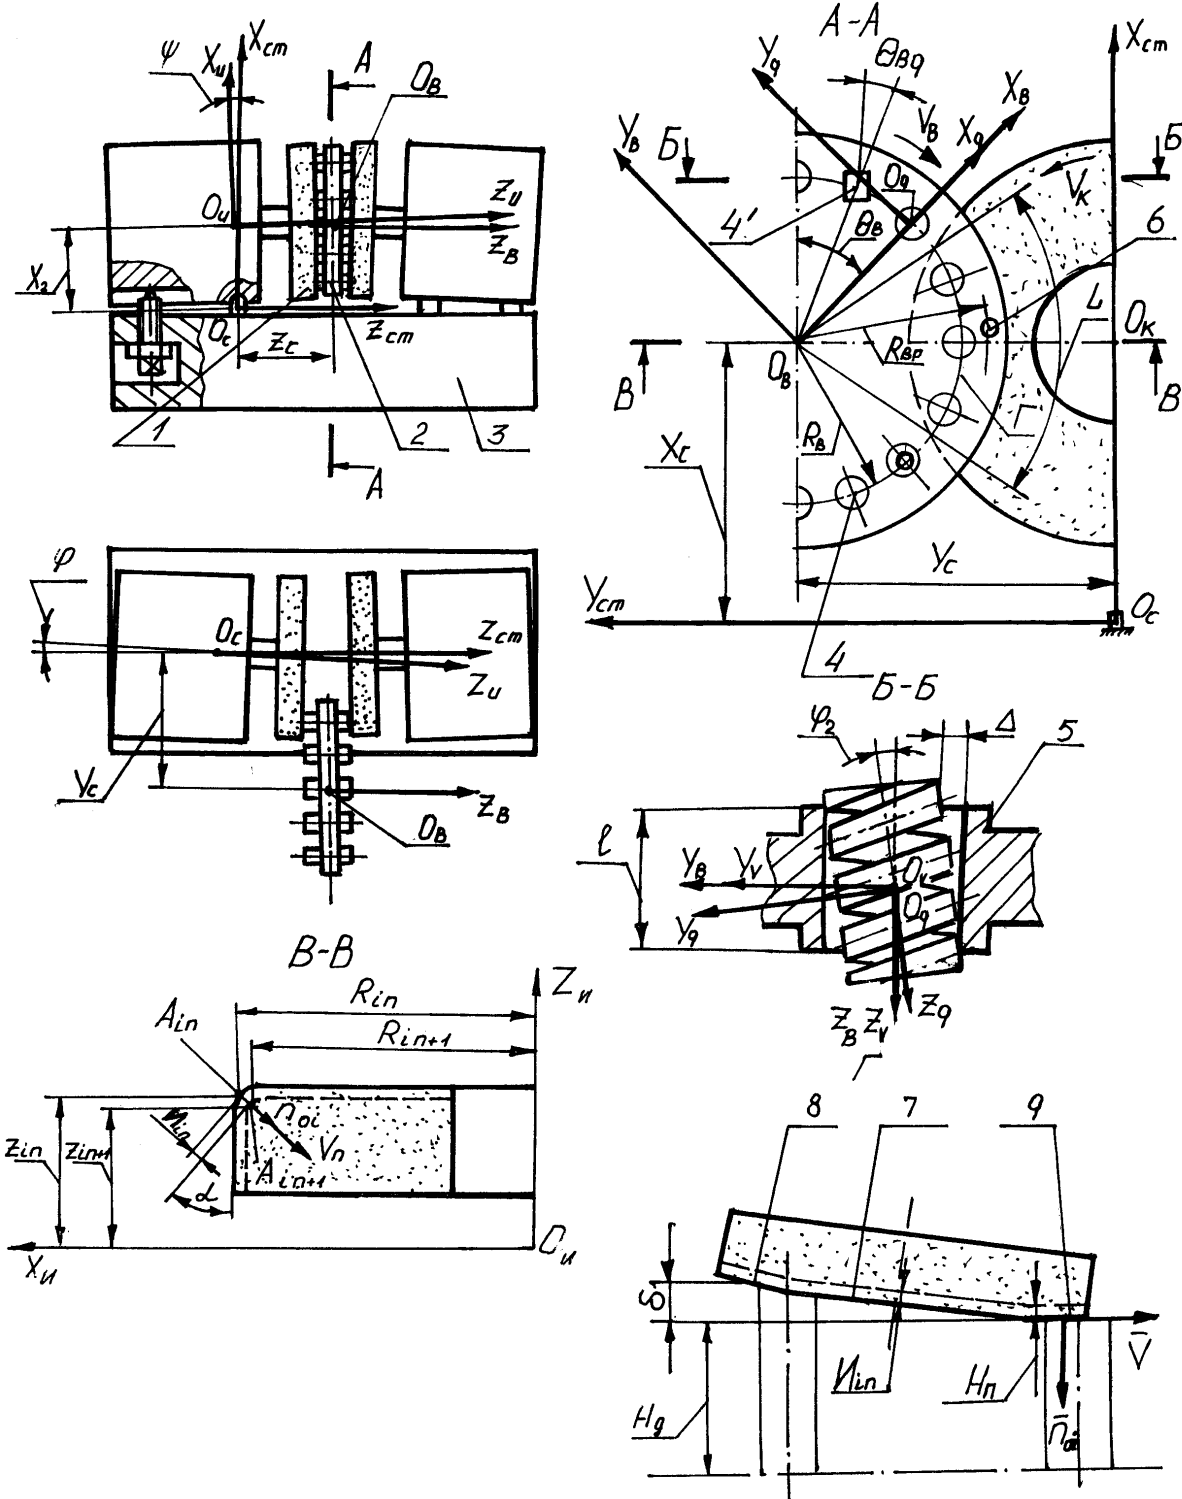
Схема формуючої системи верстату для шліфування торців зі схрещеними осями кругів та деталей
